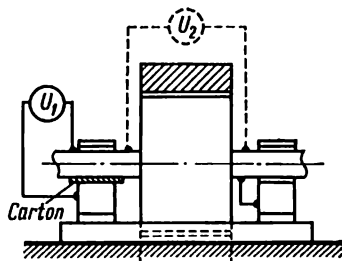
Isolation de l'arbre du rotor pour le séchage de la machine
